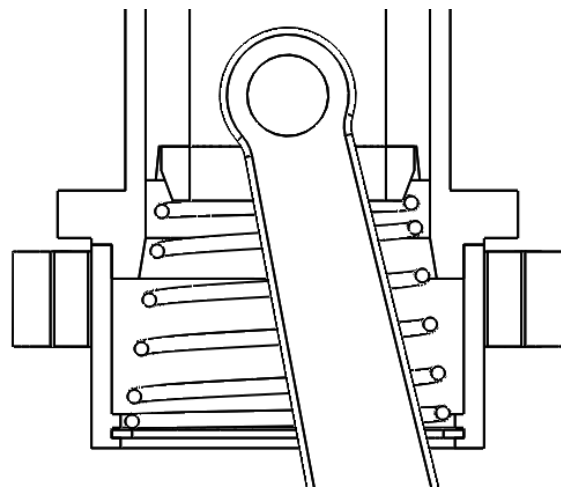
Reprezentare CAD a variantei constructive ce conține arcul, elementele de montaj și componentele care susțin elementele de montaj
